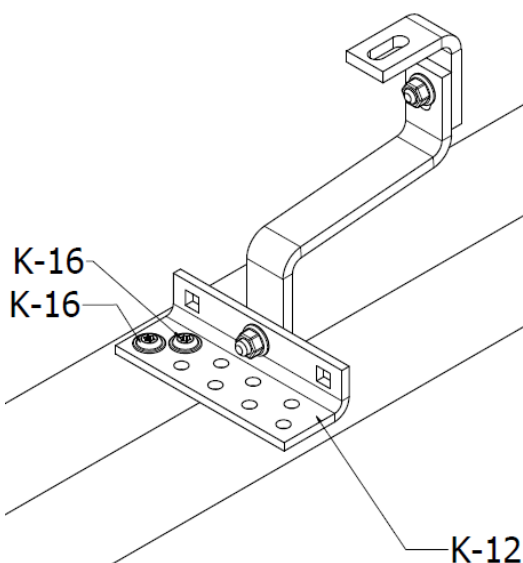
Schemat sposobu montażu uchwyty – montaż po krótkim boku modułów
